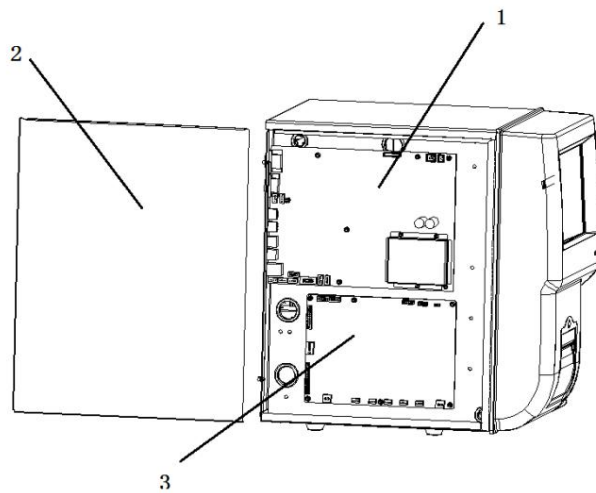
Vue du côté gauche de l'unité principale ouverte
